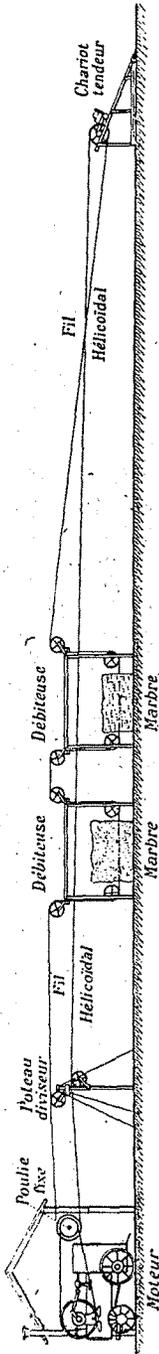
Installation du fil hélicoïdal dans une carrière.
